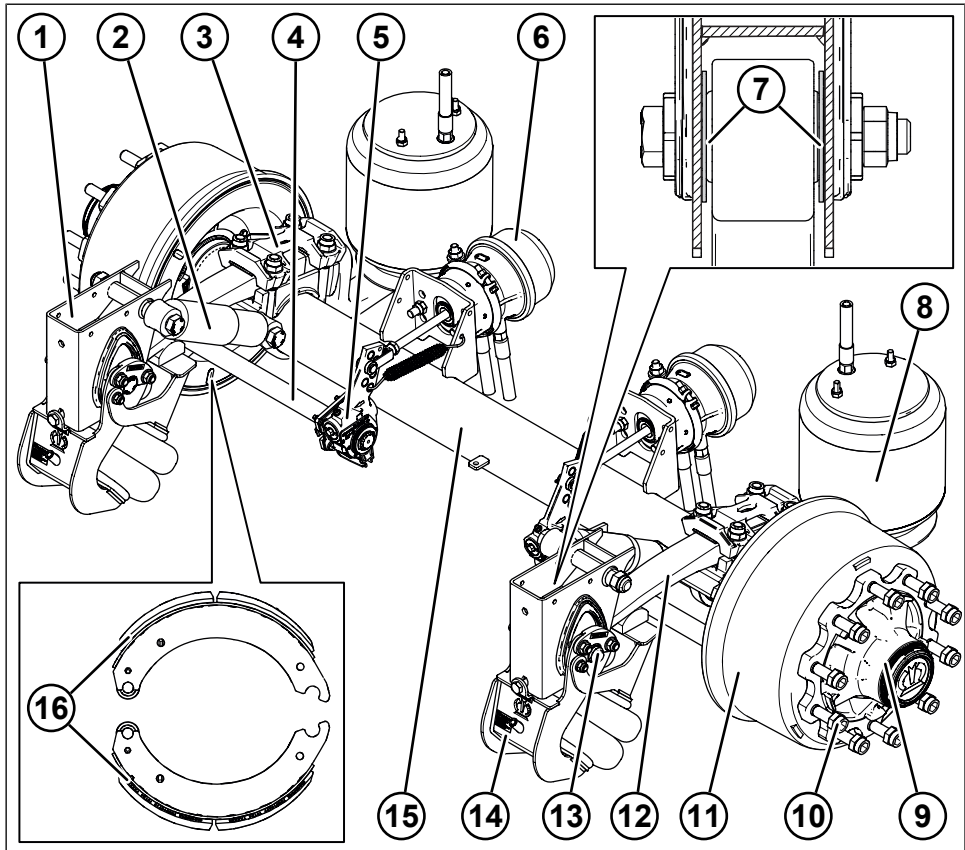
Vue d'ensemble de la maintenance du frein à tambour
